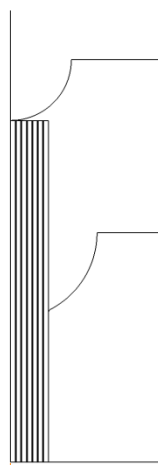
Комп'ютерна модель заготовки і деформуючого інструменту
